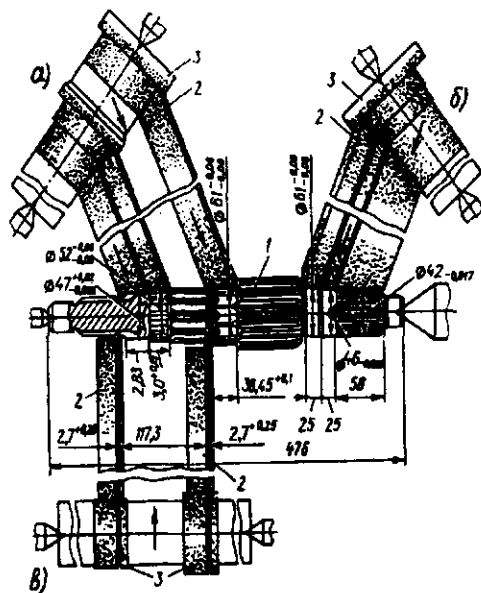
Схемы совмещенного шлифования шеек и торцов вторичного вала коробки передач автомобиля ЗИЛ-130: 1 – обрабатываемая деталь; 2 – шлифовальные круги; 3 – алмазные правящие ролики
